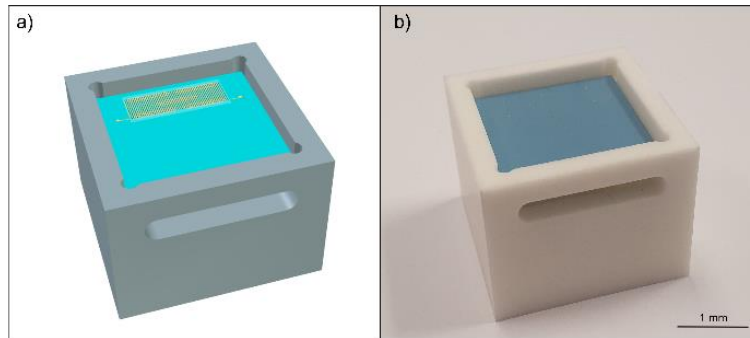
a) CAD-Zeichnung des Gehäuses mit Sensorchip, b) hergestelltes Gehäuse mit eingesetztem Sensorchip.
